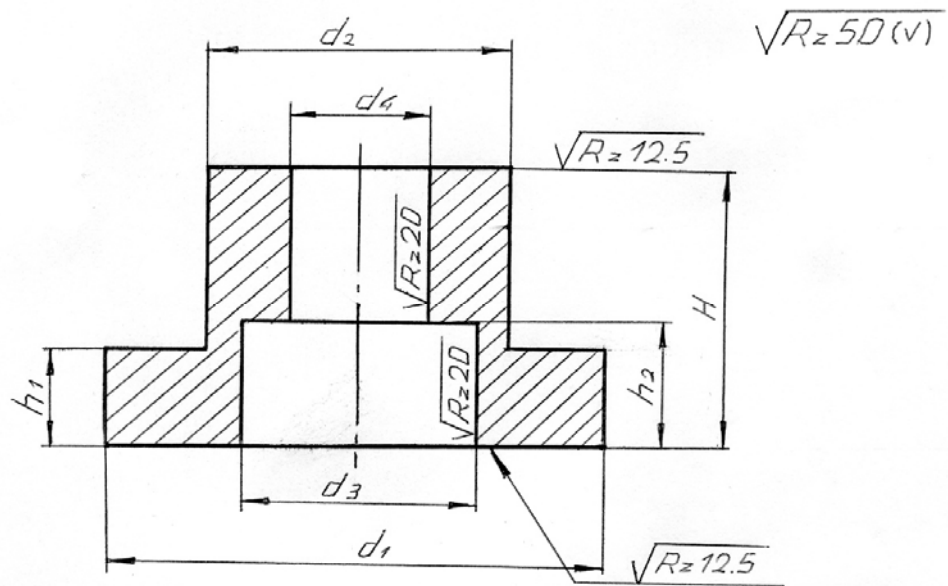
Чертёж детали: материал- сталь 45л;
